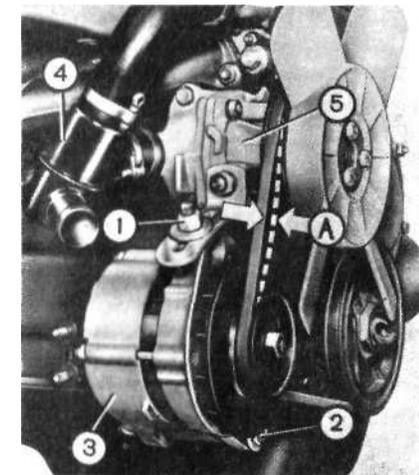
Проверка натяжения ремня генератора и вентилятора
